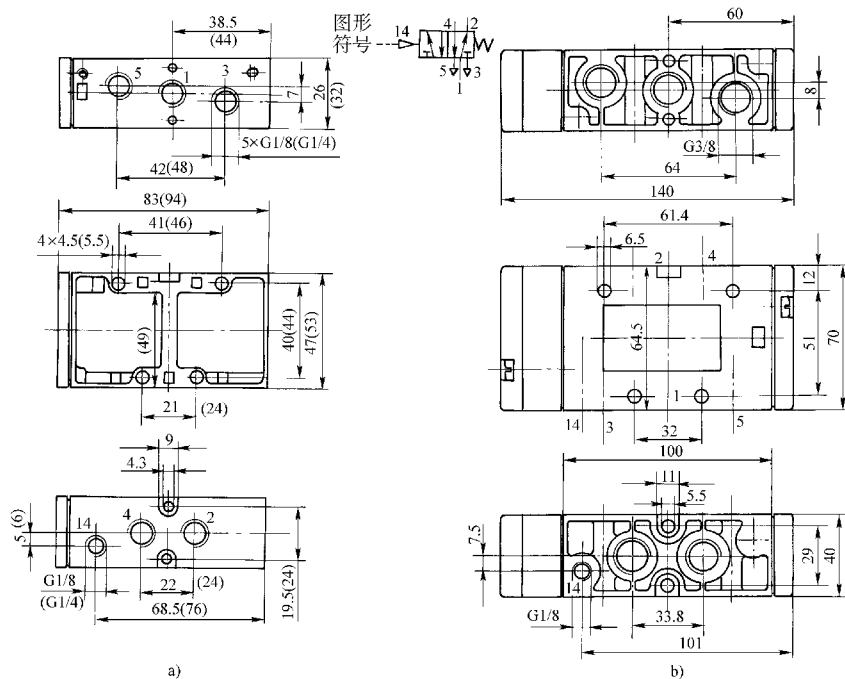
VL 系列二位五通单气控换向阀外形尺寸
